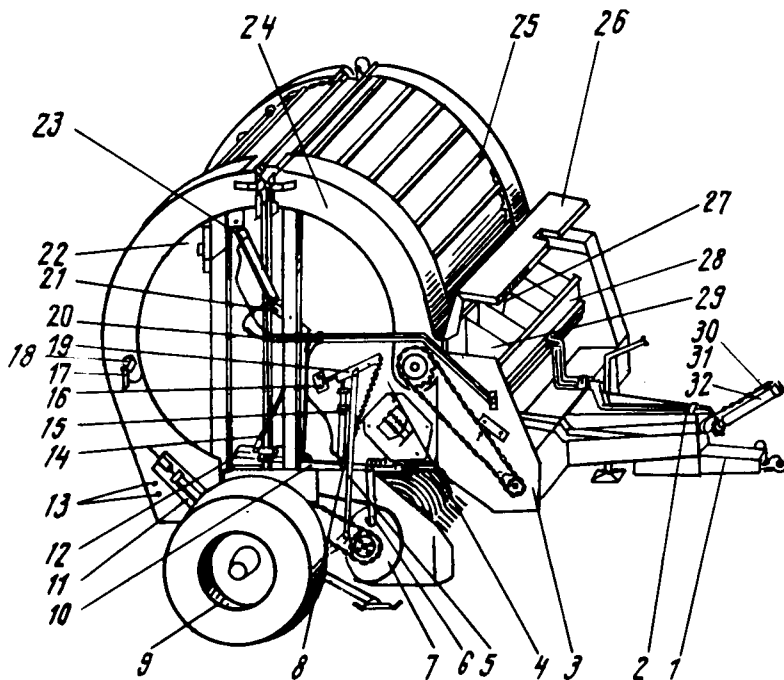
Камера прессования пресс-подборщика ПР-Φ-750: 1 - сница; 2 - тормозная система; 3 - лобовина; 4 - механизм регулирования плотности прессования; 5 - тяга; 6 - защелка; 7 - подборщик; 8 - винт; 9 - основание камеры с колесным ходом; 10 - трос; 11 - натяжная ось; 12 - защелка; 13 - отверстие; 14 - тяга; 15 - гидроцилиндр; 16 - упор; 17 - кронштейн; 18 - фонарь; 19 - рычаг; 20 - тяга; 21 - рычаг; 22 - задняя часть прессовальной камеры; 23 - гидроцилиндр; 24 - передняя часть прессовальной камеры; 25 - пружина; 26 - крышка ящика; 27 - подпорка; 28 - ящик; 29 - отсек ящика; 30 - трос страховочный; 31 - гидросистема; 32 - карданная передача
